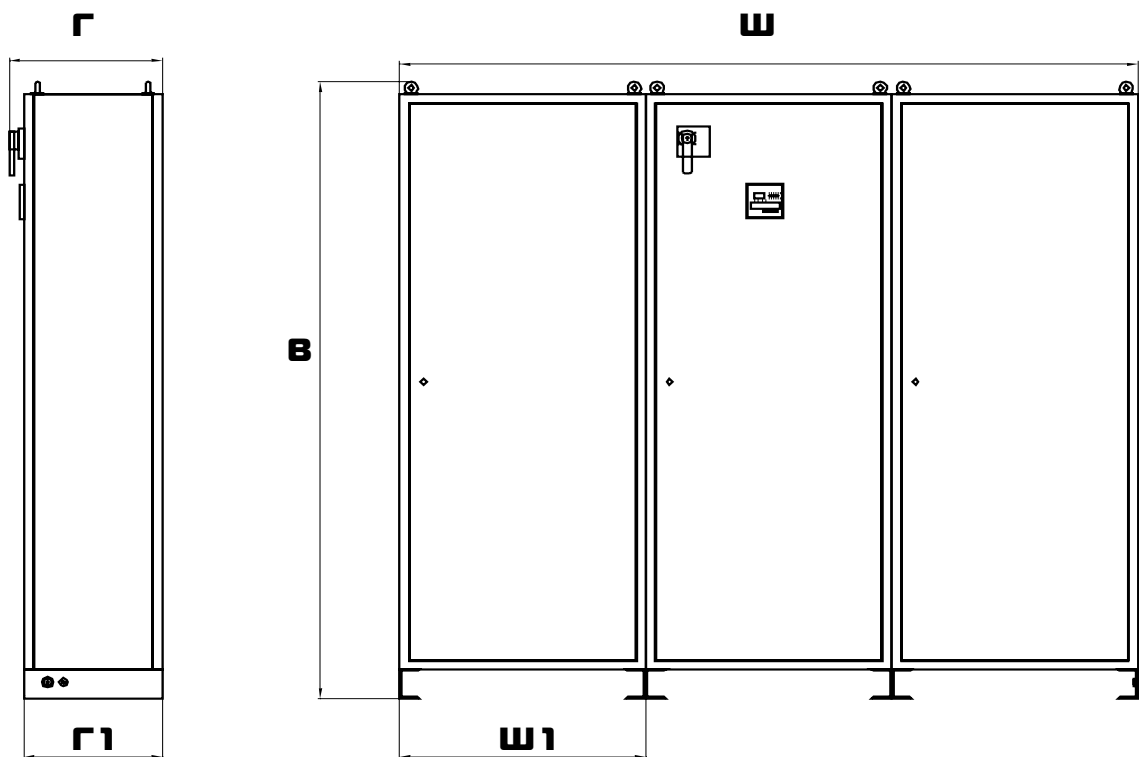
Габаритный чертеж КРМ-0,4 (900-1000 кВАр) IP20, IP40
